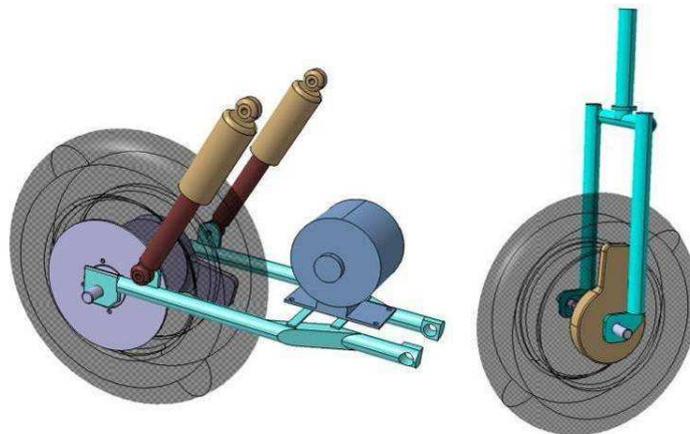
Modelos en CAD de las llantas, suspensiones y motor.
